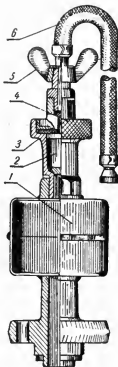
Приспособление для накачивания шин к трактору «Беларусь»:
